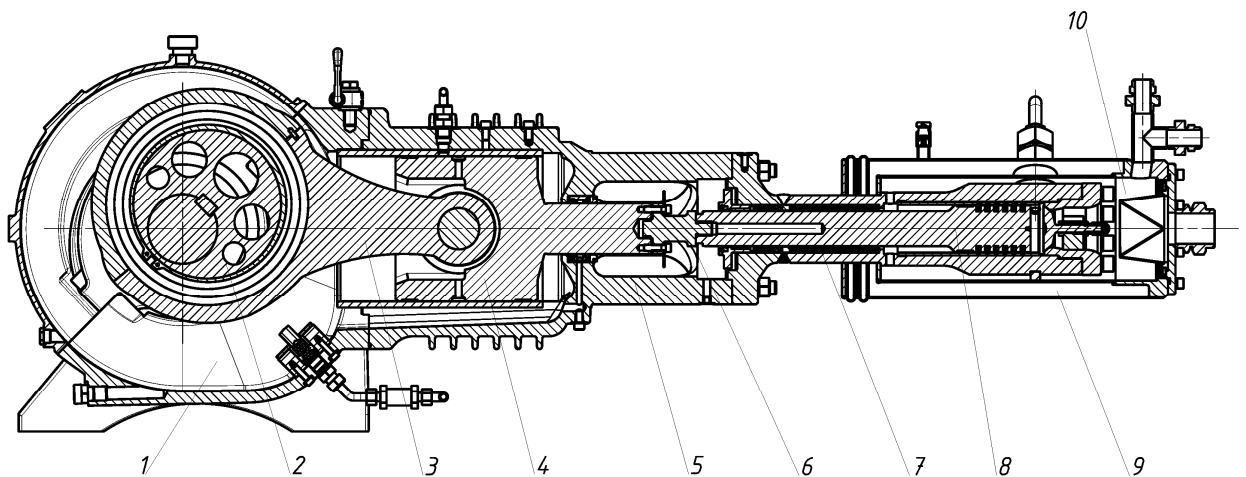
Газовий компресор високого тиску серії HPP3 60/110 фірми Cryostar. 1 – кривошипна камера; 2 – кривошип; 3 – шатун; 4 – крєйцкопф; 5 – ущільнювальна камера; 6 – шток привода робочого поршня; 7 – робочий циліндр із системою ущільнень; 8 – робочий поршень; 9 – вакуумна теплоізолююча камера; 10 – прийомна камера
